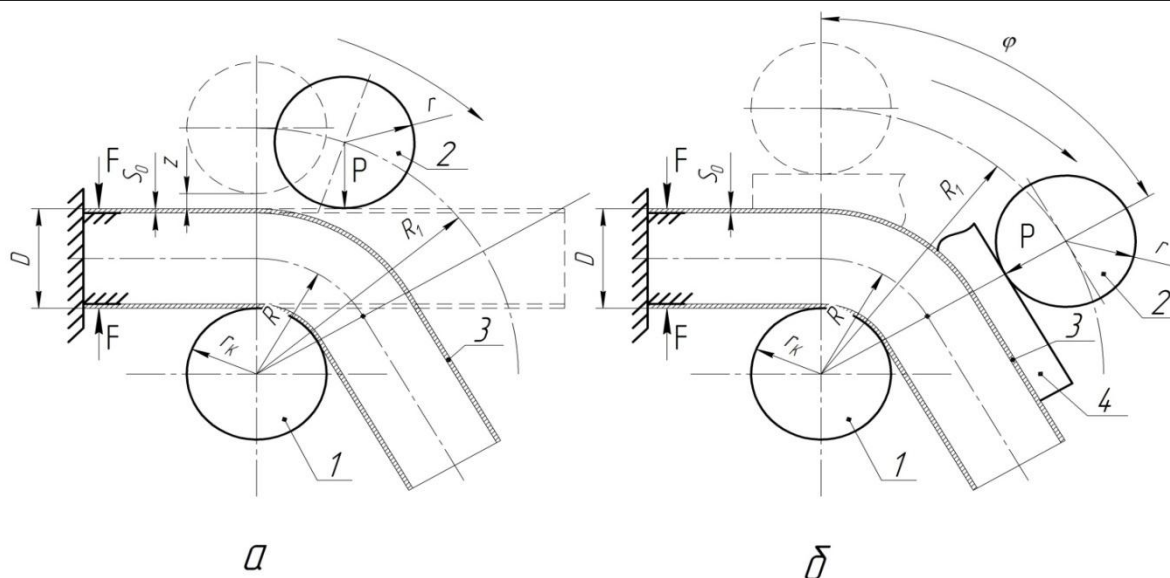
Схемы гибки обкаткой: а – с зазором z; б – с использованием лотка
